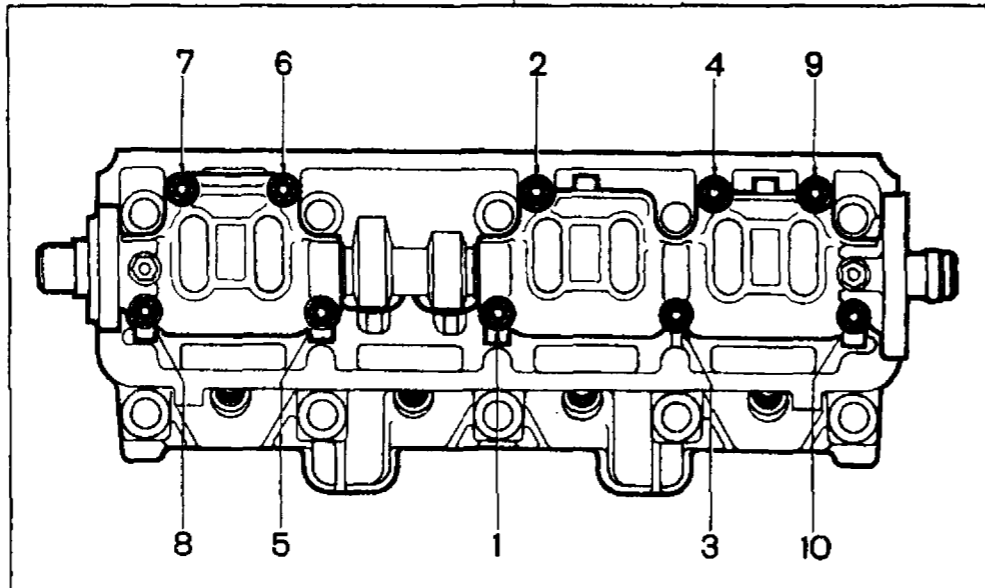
Порядок затягивания гаек крепления корпусов подшипников распределительного вала
